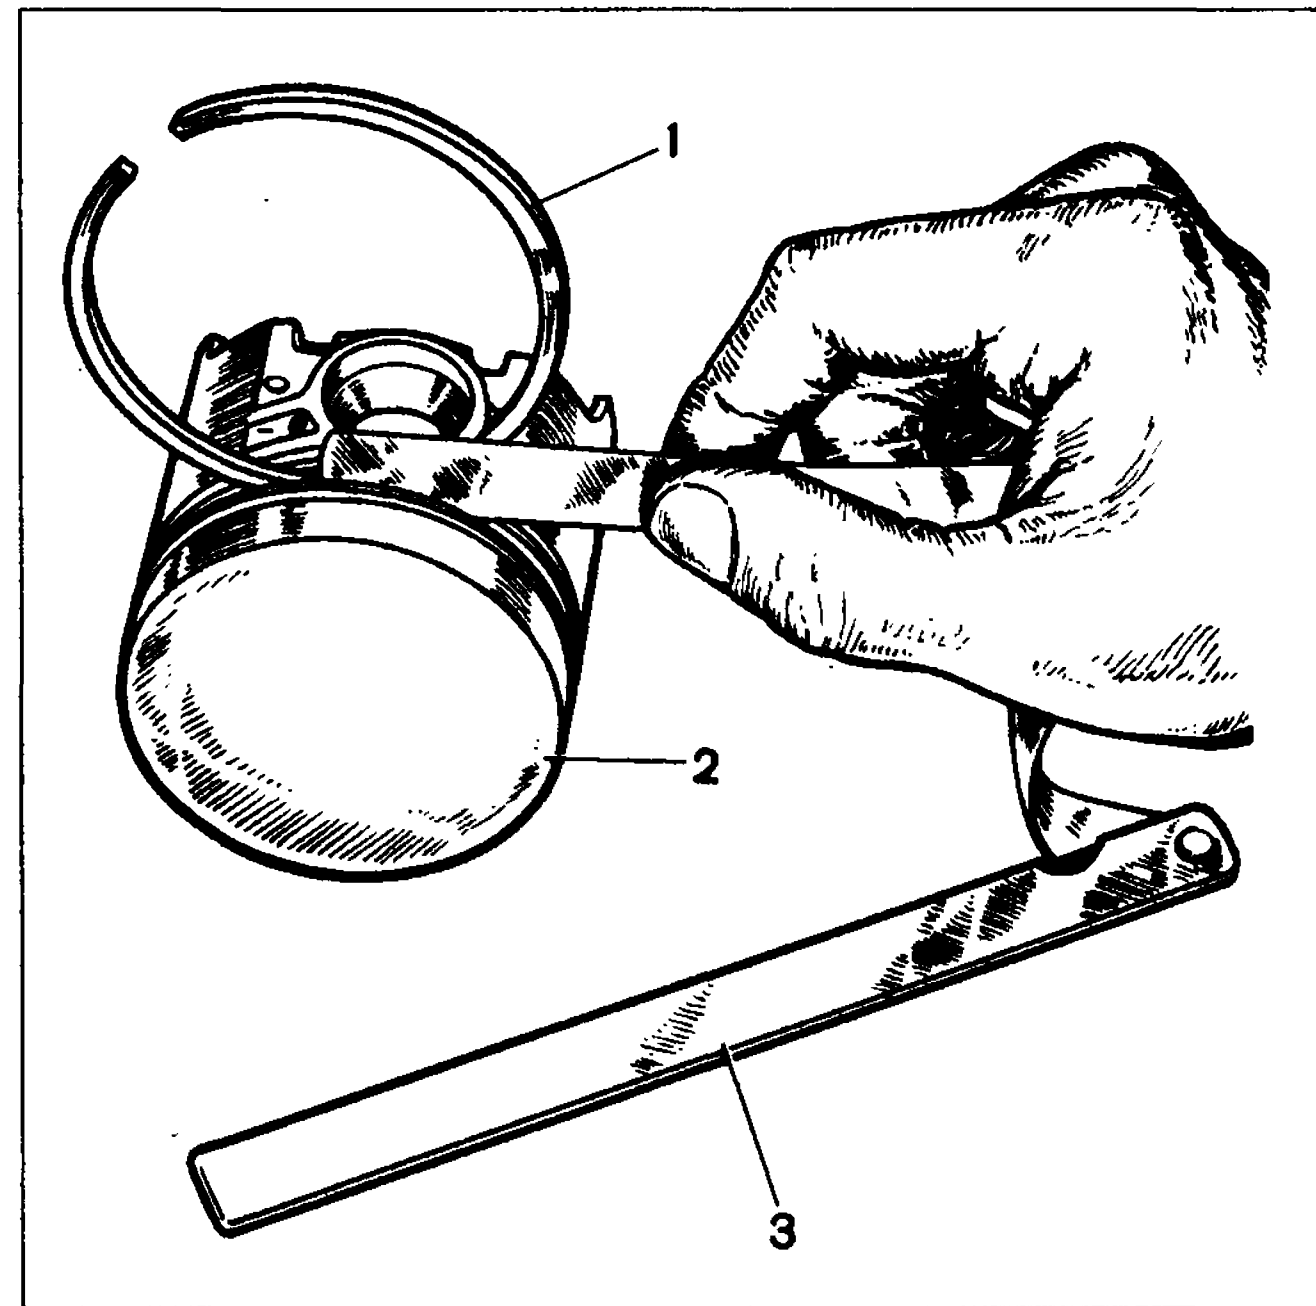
Проверка зазора между поршневыми кольцами и канавками:
